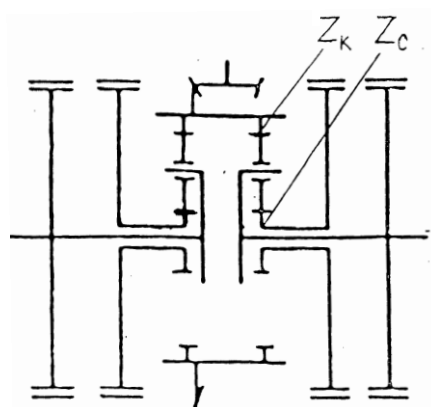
Схема планетарного редуктора гусеничного трактора
